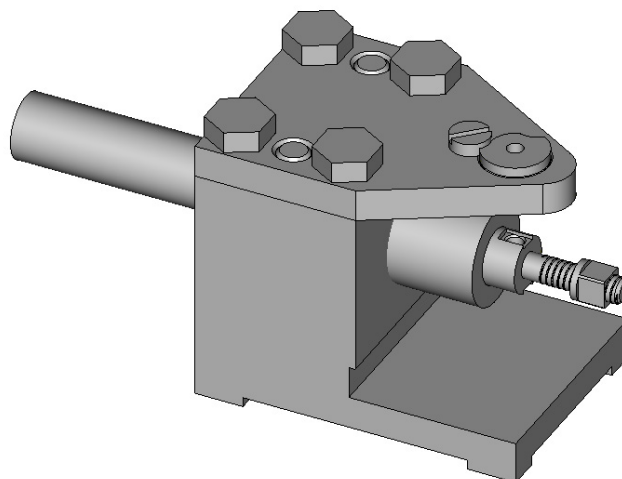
Кондуктор для сверления отверстия в заготовке типа «цилиндр»
